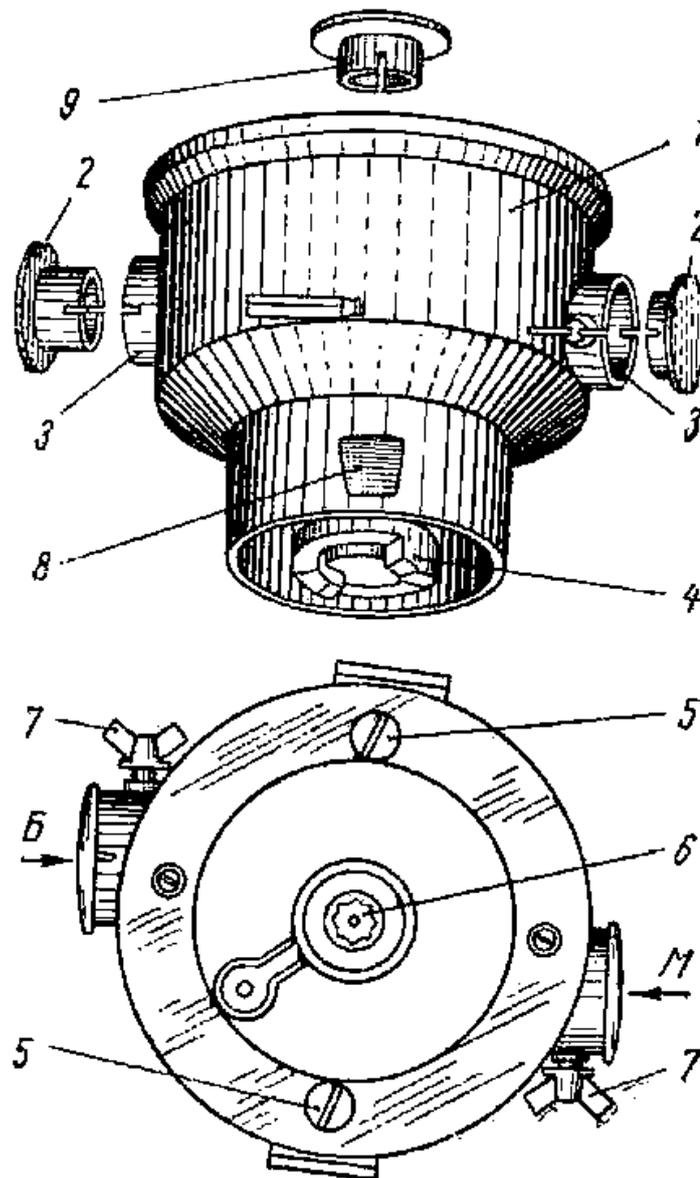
Редуктор: 1 — корпус; 2 и 9 — защитные колпачки; 3 — боковое гнездо; 4 — муфта; 5 — винт; 6 - верхнее гнездо; 7 ~ винт-барашек; 8 — выступ
